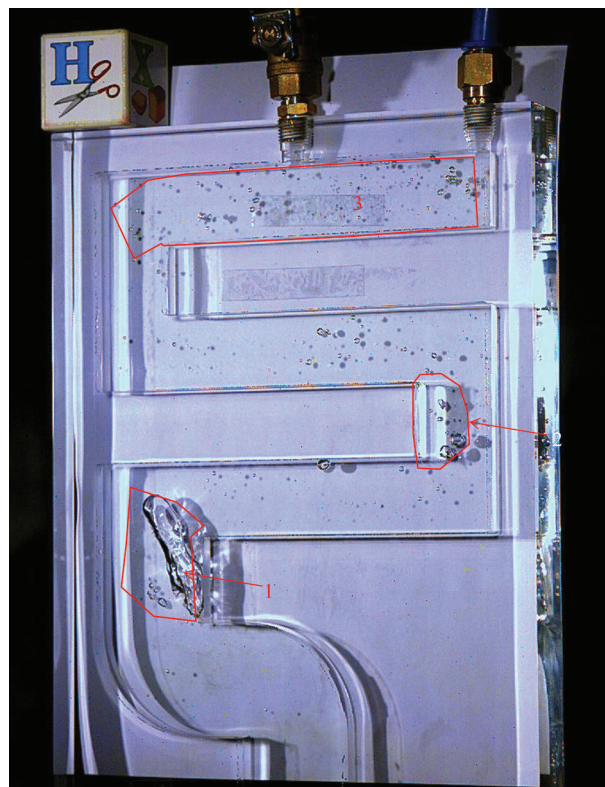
Завершение процесса заполнения: 1, 2, 3 – области возможного формирования раковин и газовой пористости
